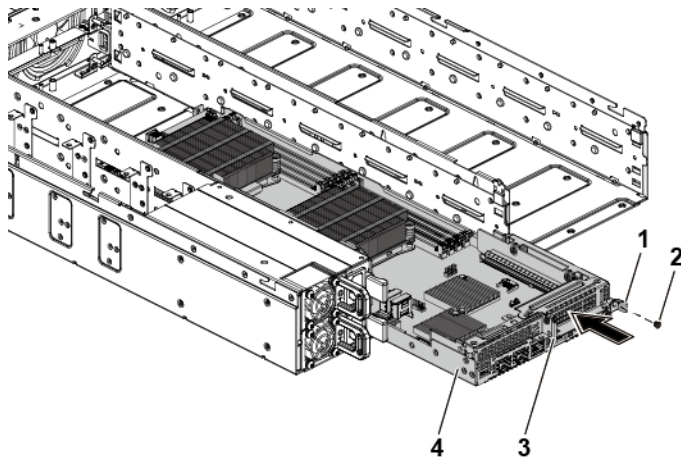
Entfernen und Einsetzen einer Systemplatinenbaugruppe
